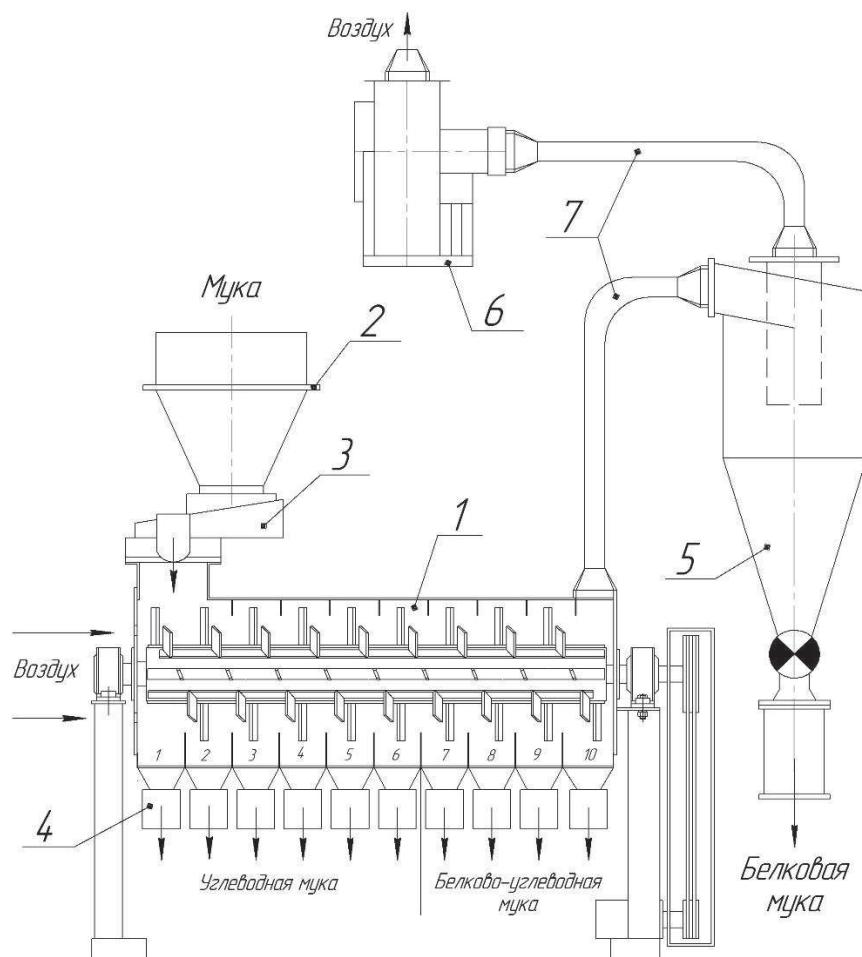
Установка центробежно-роторного пневмоклассификатора
